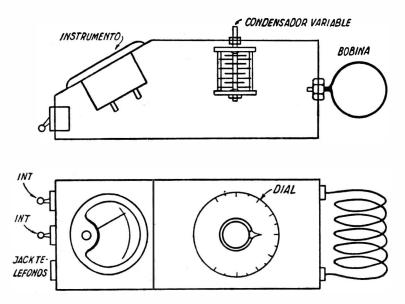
Aspecto constructivo del aparato de la figura 185.
